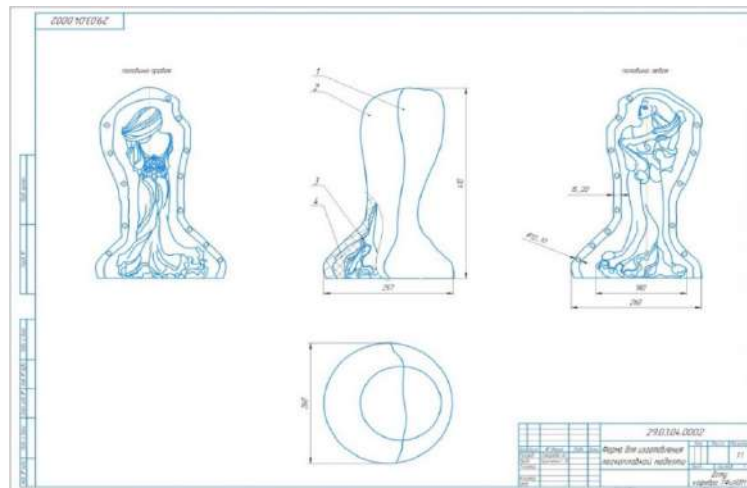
Чертеж формы для изготовления легкоплавкой модели:
